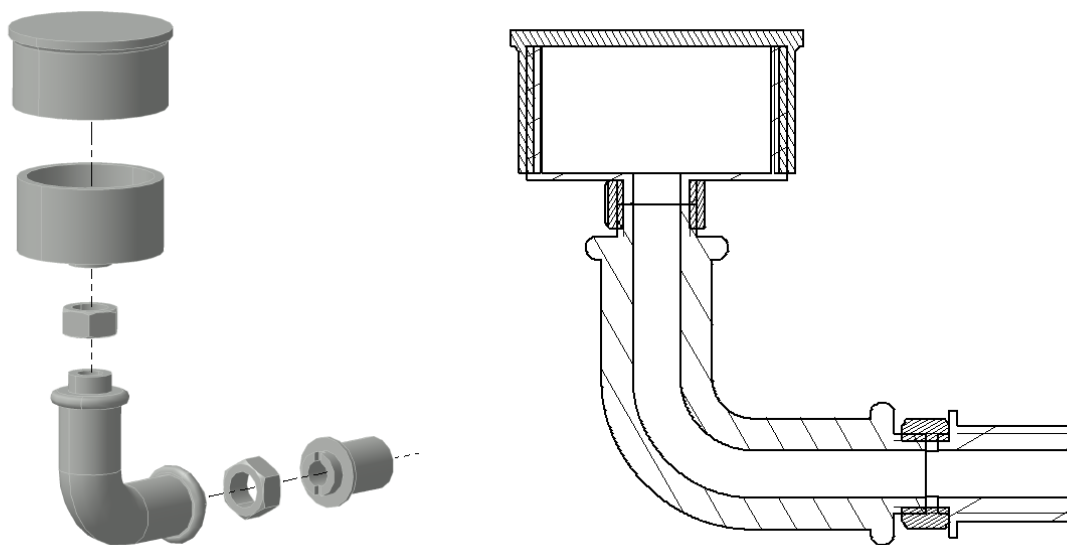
Vista explosionada y corte de una aceitera o lubricador por gravedad.
